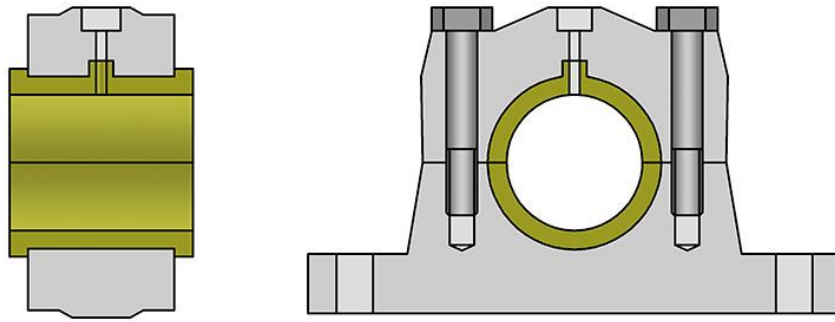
Зовнішній вигляд роз'ємного підшипника ковзання
